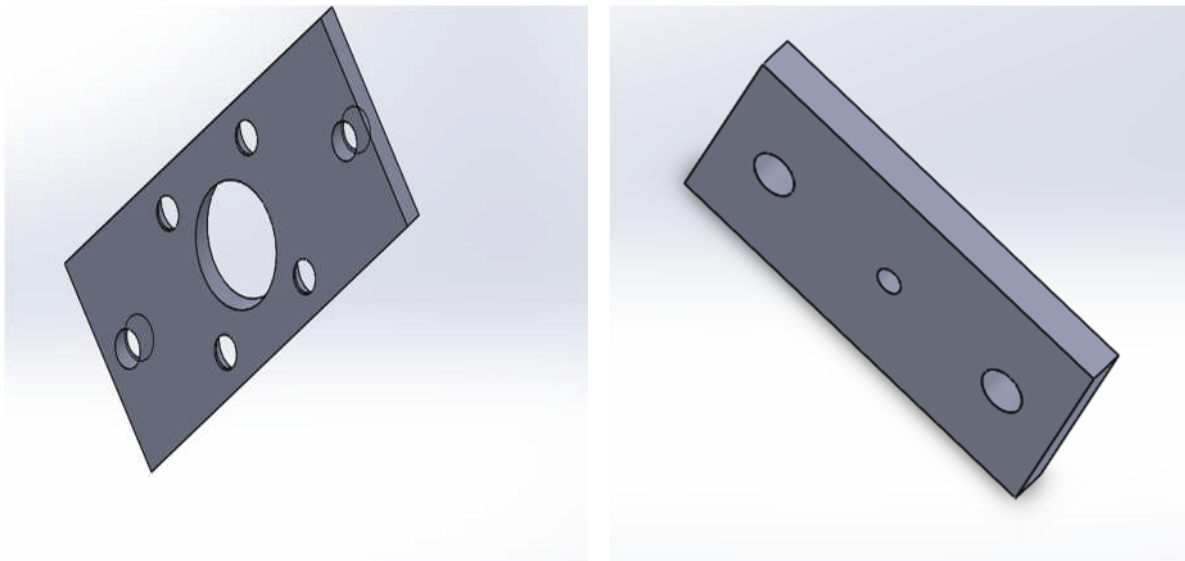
Accessoire du dispositif porte vérin de la plaque chauffante.
